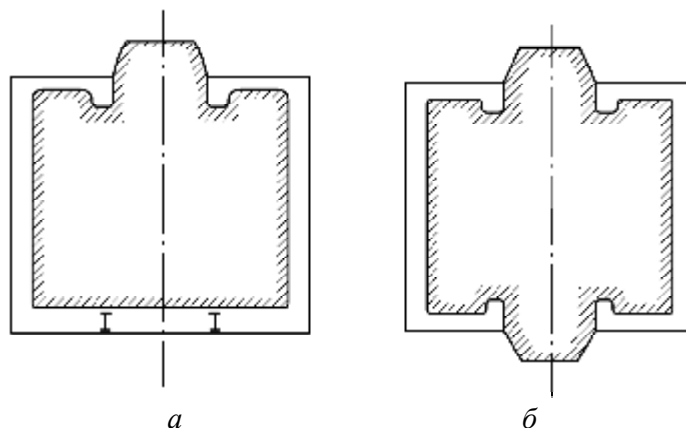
Пример устройства жеребеек и дополнительных отверстий для выхода знака стержня:
